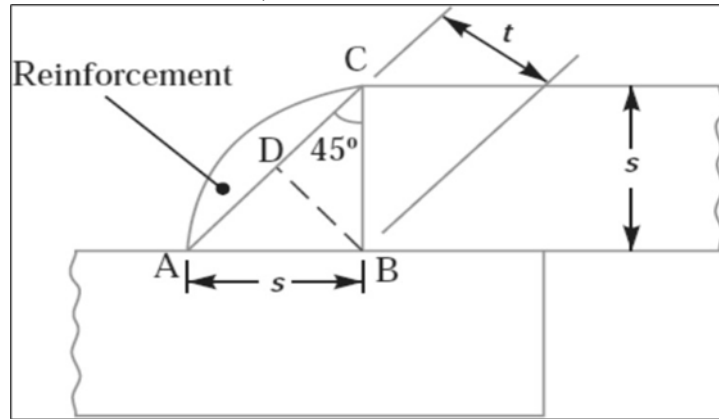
फिलेटचा मोठा दृश्य (Enlarged view of Fillet weld)
